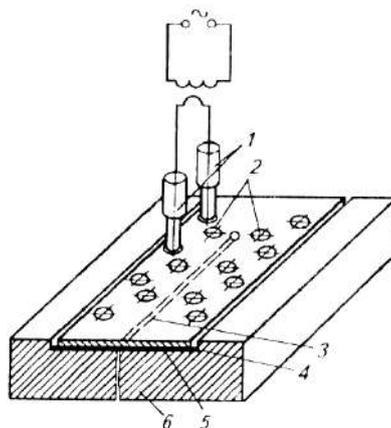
Схема заделки трещин с помощью клея и электроконтактной сварки:
